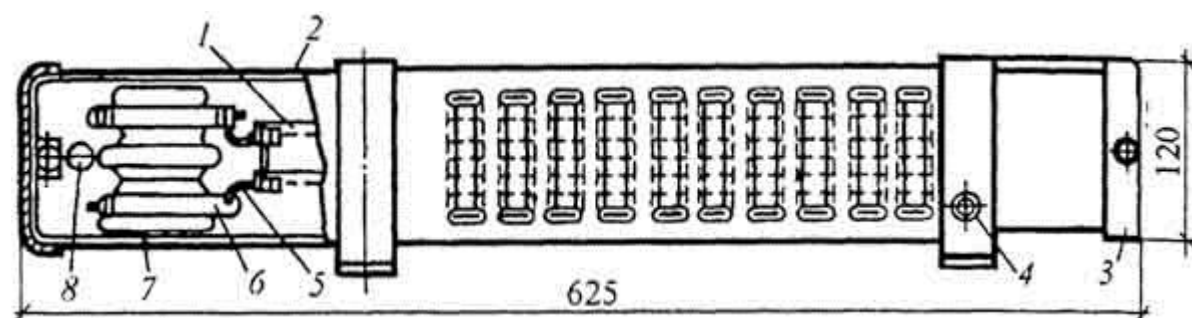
Электронагревательная печь (боковой вид): 1 - трубчатые электронагреватели; 2 - стальной кожух; 3 - крышки; 4 - контакт заземления; 5 - перемычки; 6 - токоведущие шпильки; 7 - дно; 8 - отверстие для ввода электропитания
